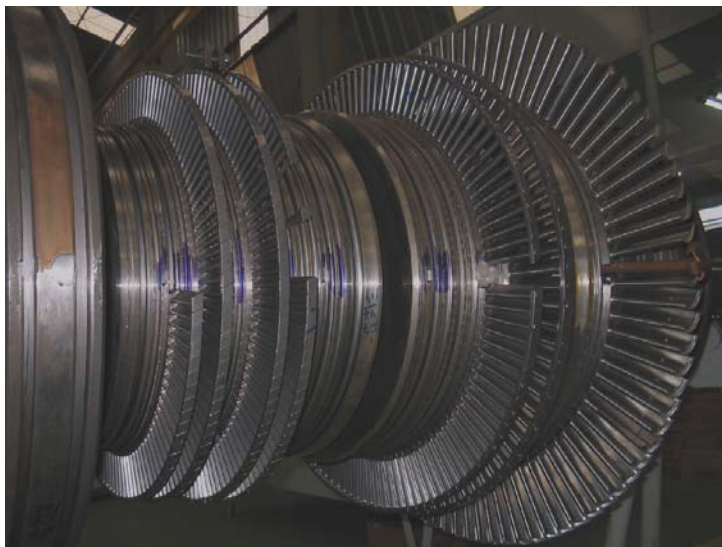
Rotor durante a recuperação, montagem de palhetas.
